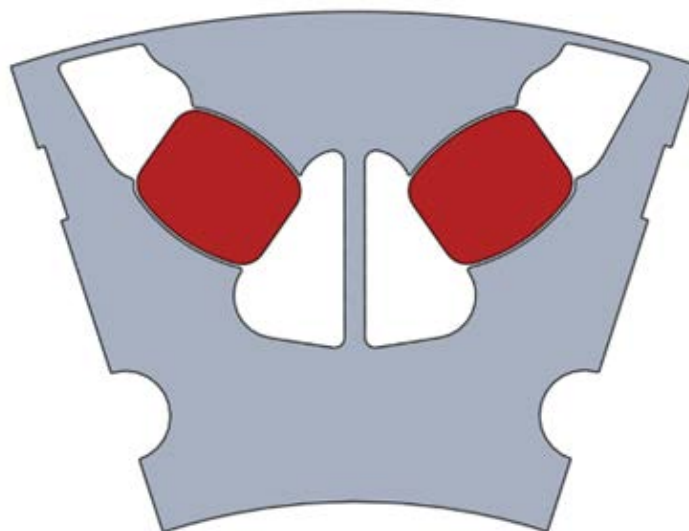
CAD-Geometrie des Rotorblechschnittes des Demonstrators
